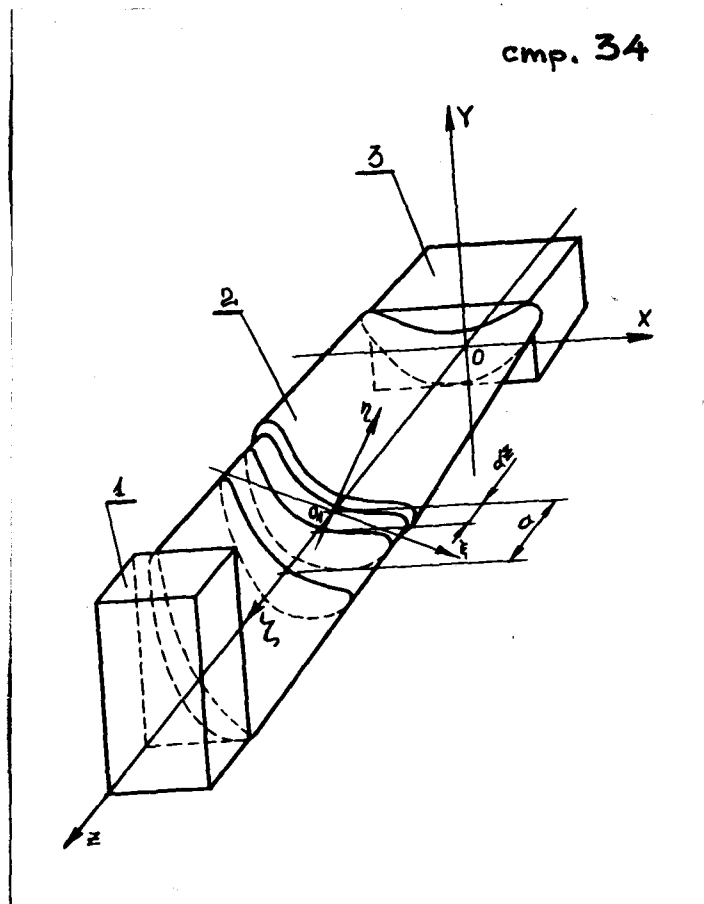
Частично обработанная заготовка турбинной лопатки
